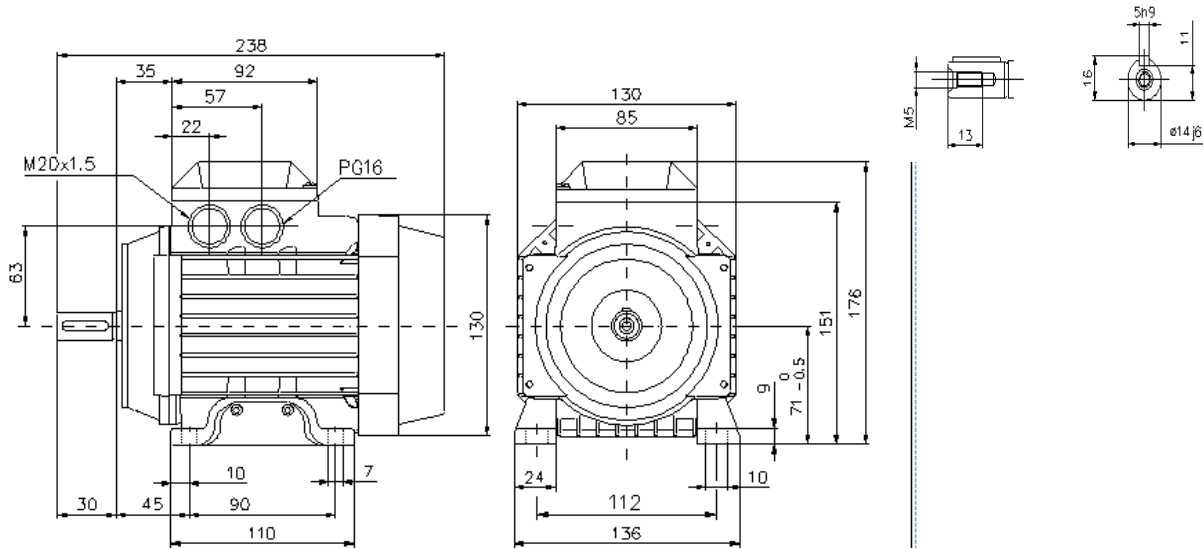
Dimensões do motor escolhido M2VA71031, [6].
